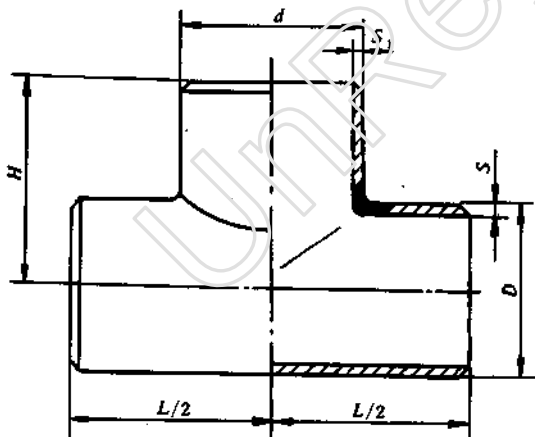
阜新电力修造厂 T 型焊制异径三通结构简图
